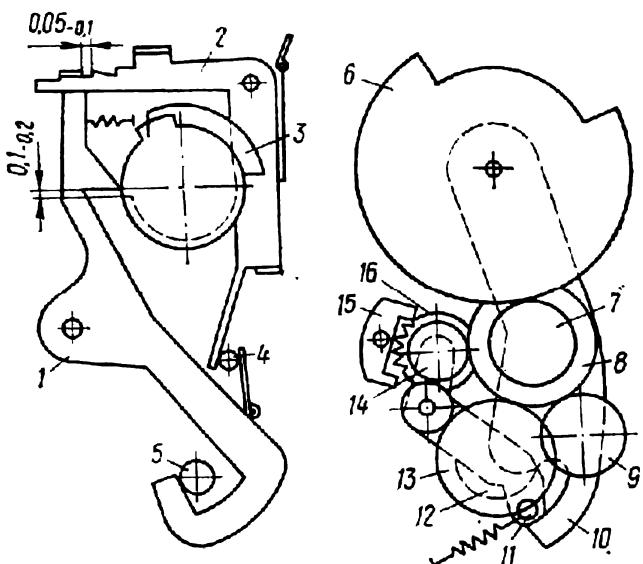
Положение деталей тормозного механизма на выдержке 1/125 с:
